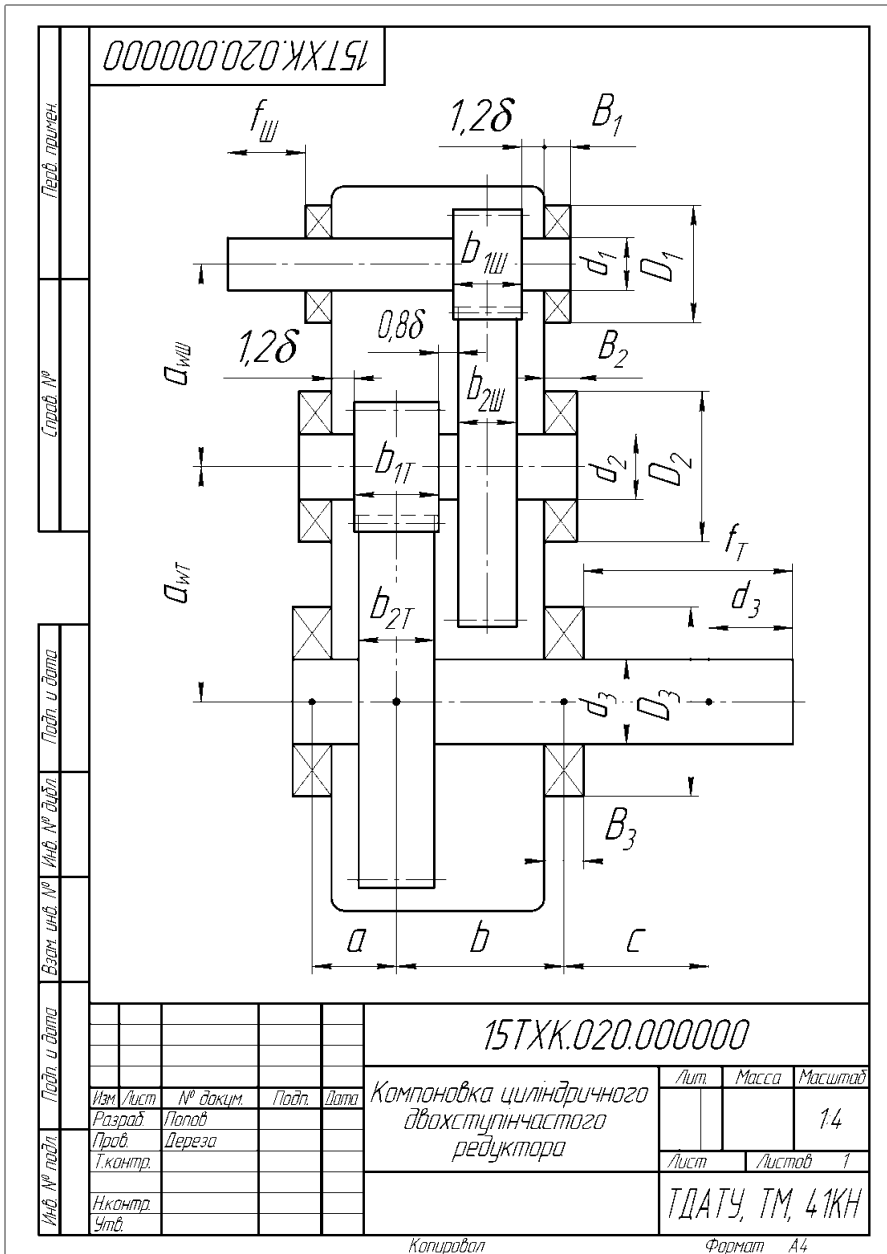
Приклад виконання ескізної компоновки редуктора
